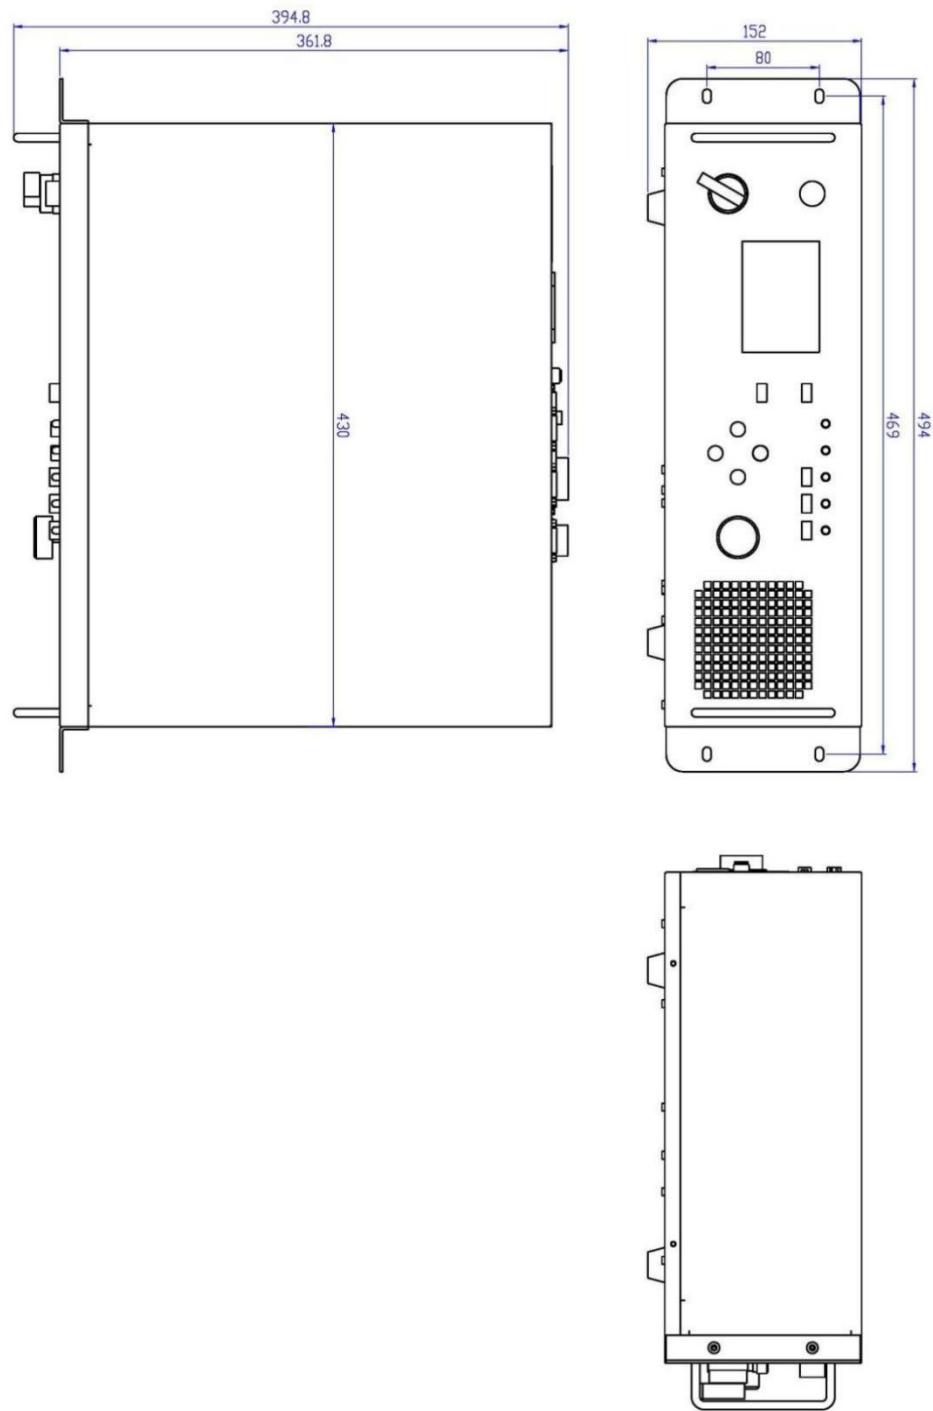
电源尺寸 Fig.9.3 Power Supply Dimensions
